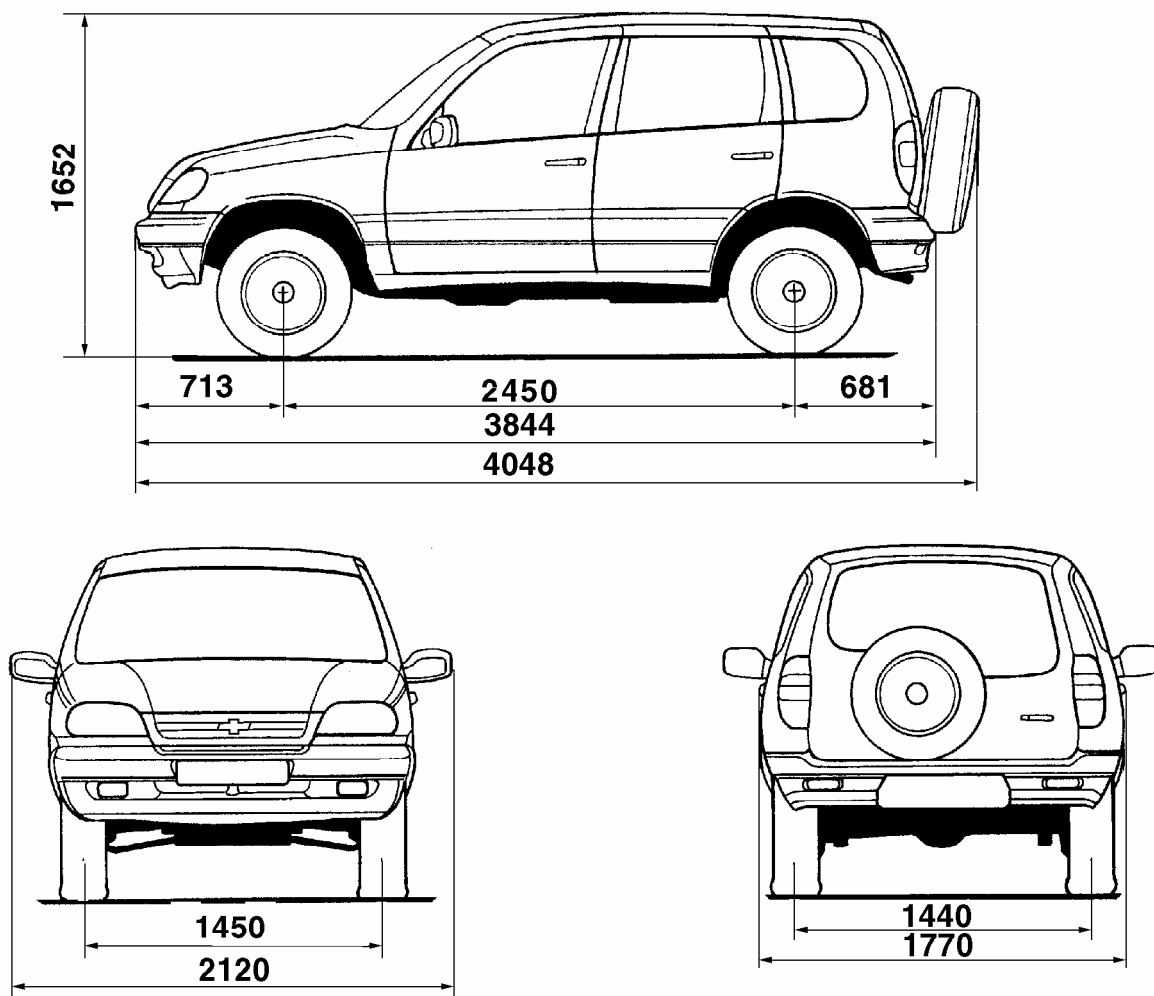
Основные габаритные размеры (справочные) автомобиля Шевроле-Нива
